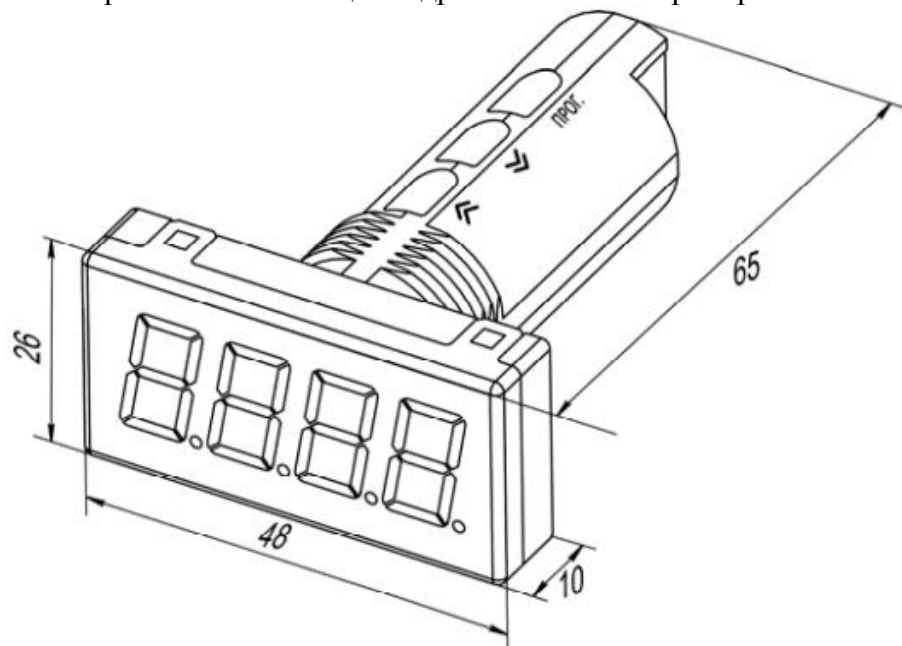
Габаритный чертеж корпуса прибора. Вид спереди.
